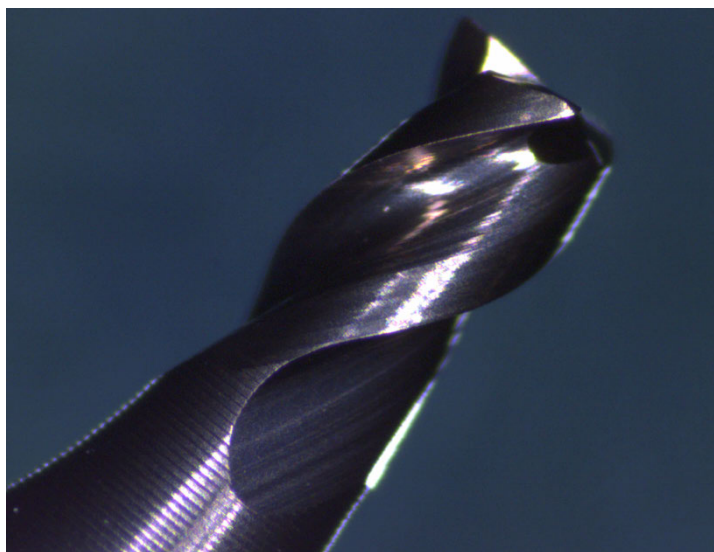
Fräswerkzeug 9 unter dem Mikroskop
